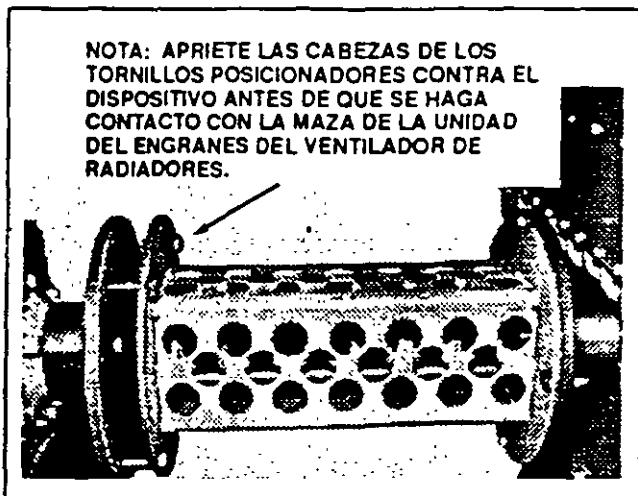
DISPOSITIVO PARA ALINEAMIENTO ATORNILLADO A LA MAZA DE SALIDA DEL COMPRESOR. E-27774-S
